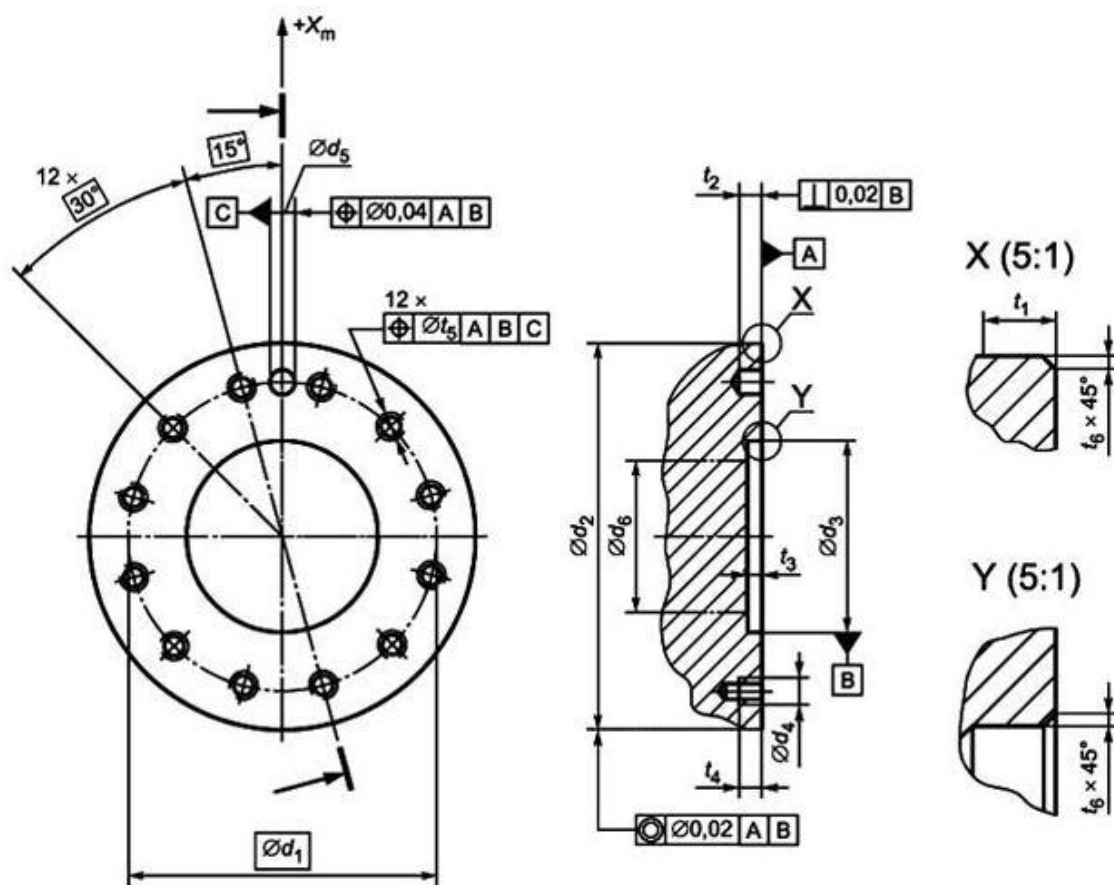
Эскиз присоединительного фланца робота-манипулятора ($d_1 = 250$ мм)
